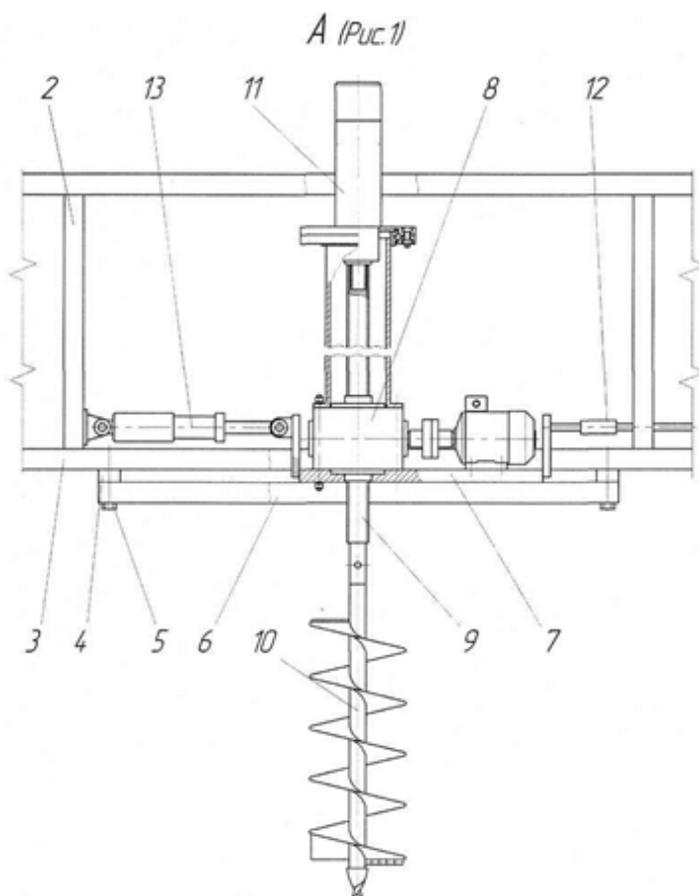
Устройство содержит энергетическое средство 1, на остова которого размещены фермы 2 прямоугольного сечения. На нижних балках 3 фермы посредством распорных пластин 4 и болтов 5 закреплены продольные балки 6. При этом между балками 3 и 6 образуется щель, в которой с возможностью перемещения, вдоль балок установлены опорные плиты 7. На опорных плитах жестко закреплены червячные редукторы 8 с приводом. Внутри полого шлицевого выходного вала редуктора размещен шлицевой вал 9, один конец которого связан с валом шнека 10, а другой со штоком гидроцилиндра 11. Опорные плиты связаны между собой регулируемые по длине тягами 12. Одна из крайних подвижных опорных плит соединен со штоком гидроцилиндра 13, проушина которого связана с фермой 2.
